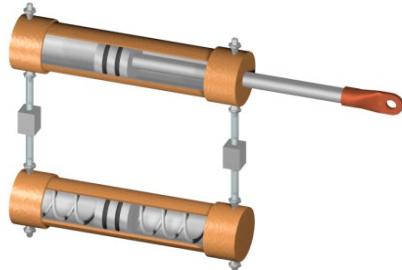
Пневмоцилиндр поршневого механизма поворота, оснащенный рекуперативно-тормозным блоком
